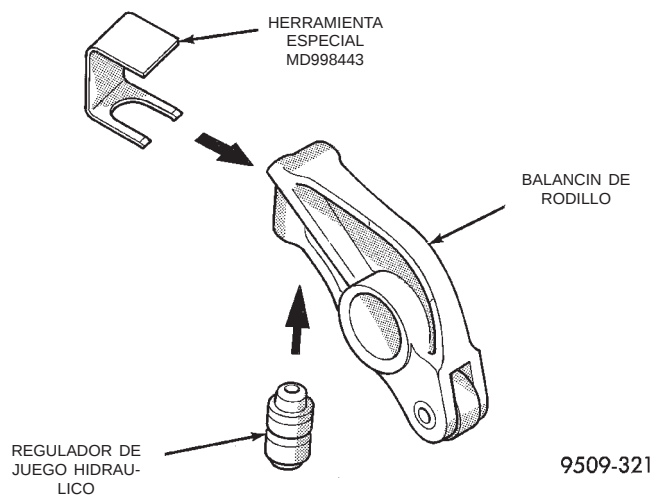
Conjunto de balancín/regulador de juego hidráulico
